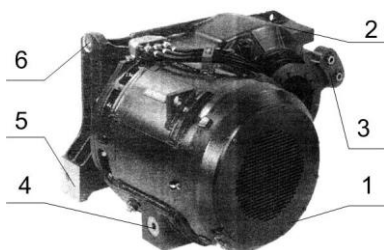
Моторно-редукторный блок завода KWD (Германия): 1 - ТЭД; 2 - редуктор; 3 - фланец поводковой муфты; 4 - опора ТЭД на раму; 5 - опора редуктора на раму; 6 - кронштейн амортизатора связи редуктора с рамой
